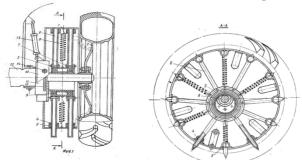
Приспособление к ведущему колесу трактора: а) вид сбоку; б) разрез A-A;
